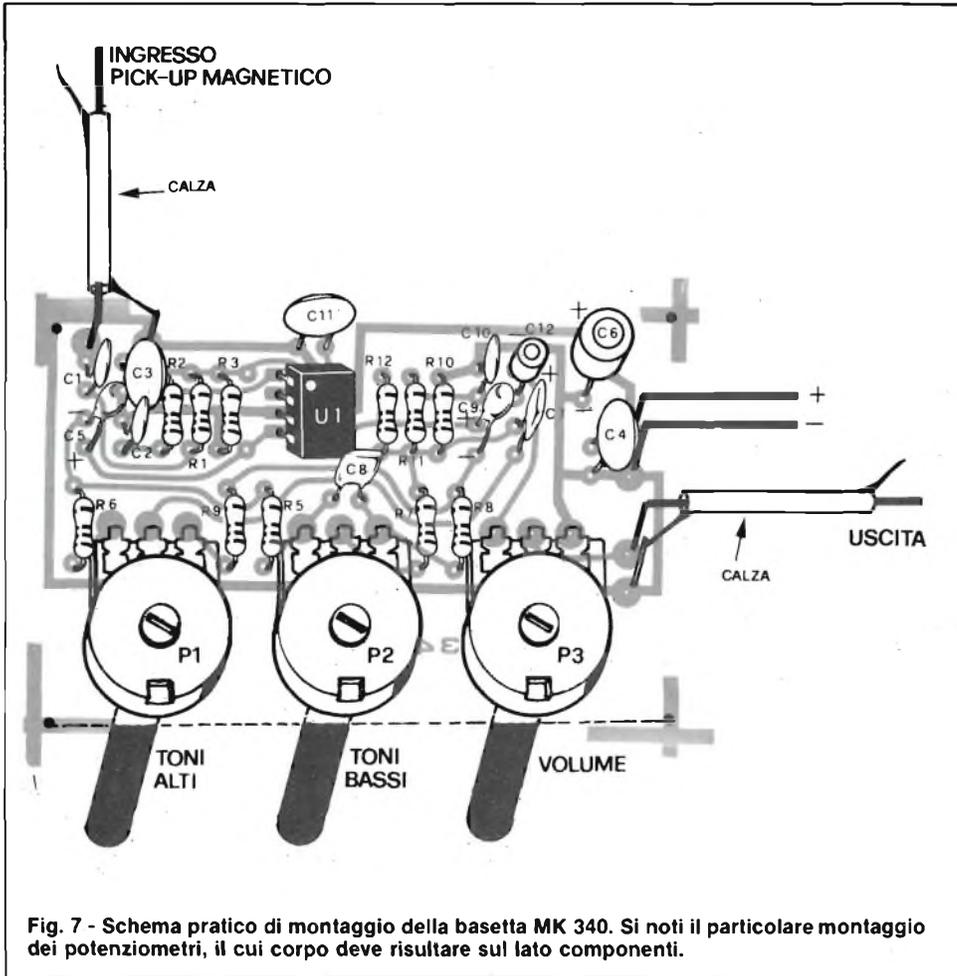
Schema pratico di montaggio della basetta MK 340. Si noti il particolare montaggio dei potenziometri, il cui corpo deve risultare sul lato componenti.
